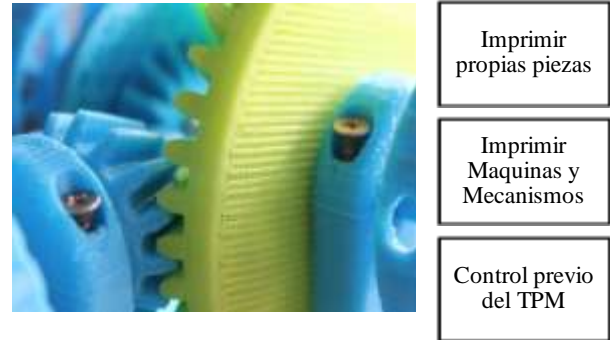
Engranajes fabricados por impresión 3D y aplicaciones
